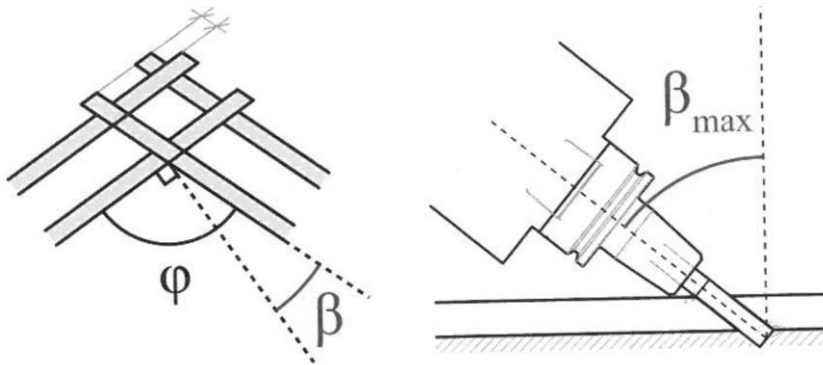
Flache Bearbeitungswinkel führen zu grossen Fräserlängen
